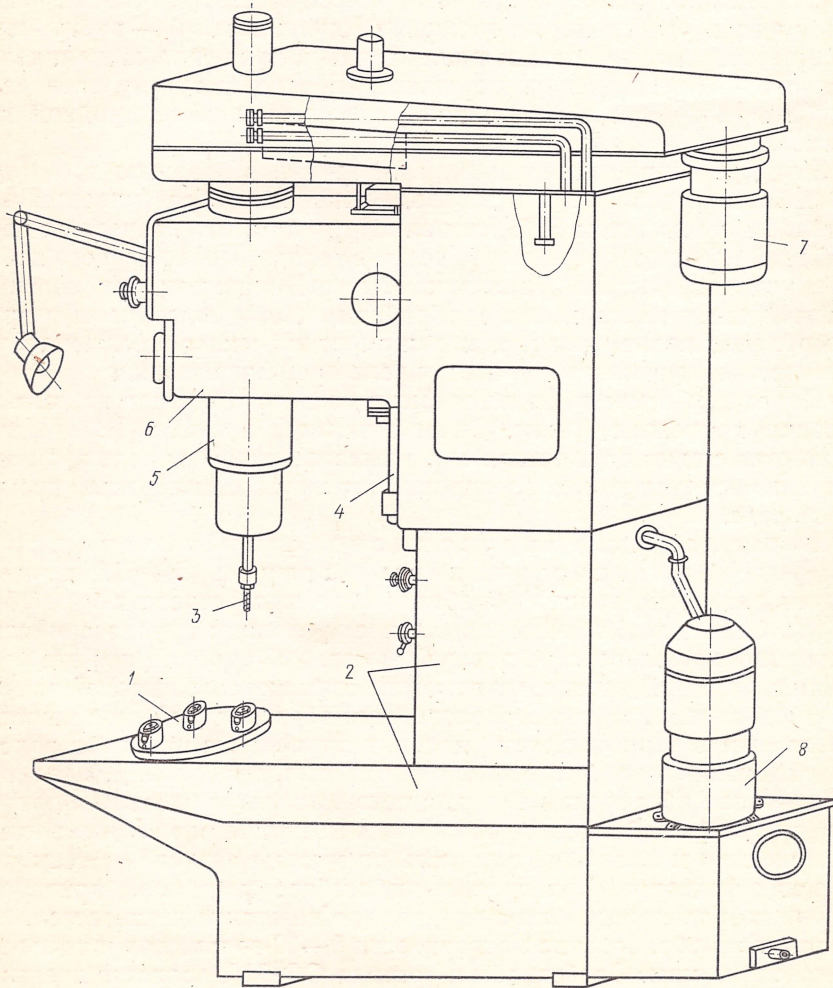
Вертикальный внутриводочный одношпиндельный многопозиционный станок ОФ-61А
